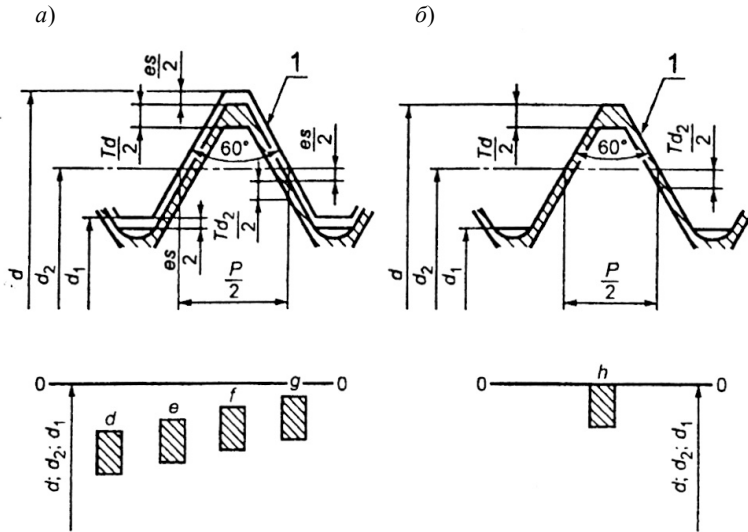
Положения полей допусков наружной резьбы:
